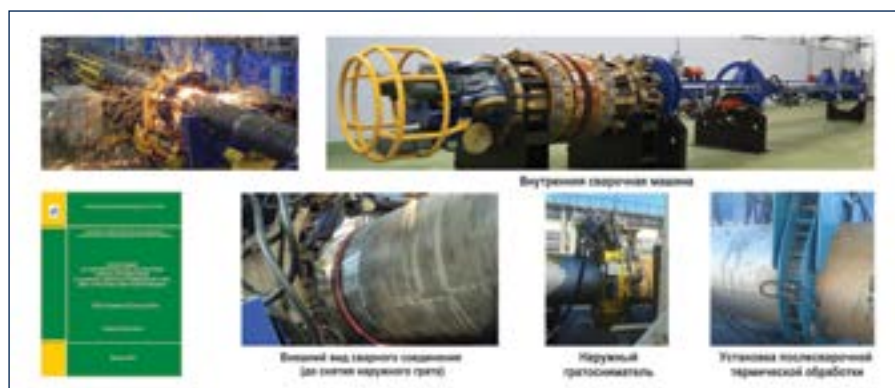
Комплекс автоматической контактной стыковой сварки оплавлением (КСО) труб большого диаметра от DN 1000 до DN 1400 (производства ЗАО «Псковэлектросвар»)
